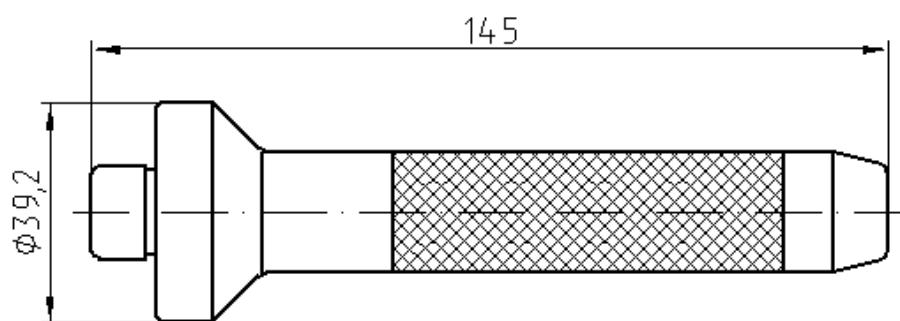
5-У-10897, Оправка для запрессовки и выпрессовки подшипника первичного вала коробки передач
